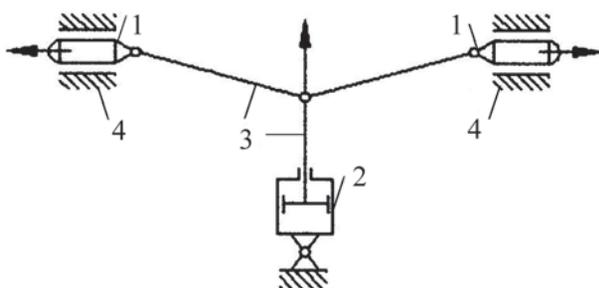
Схема использования рычажно-шарнирного механизма: 1 — плунжеры; 2 — гидропривод;
